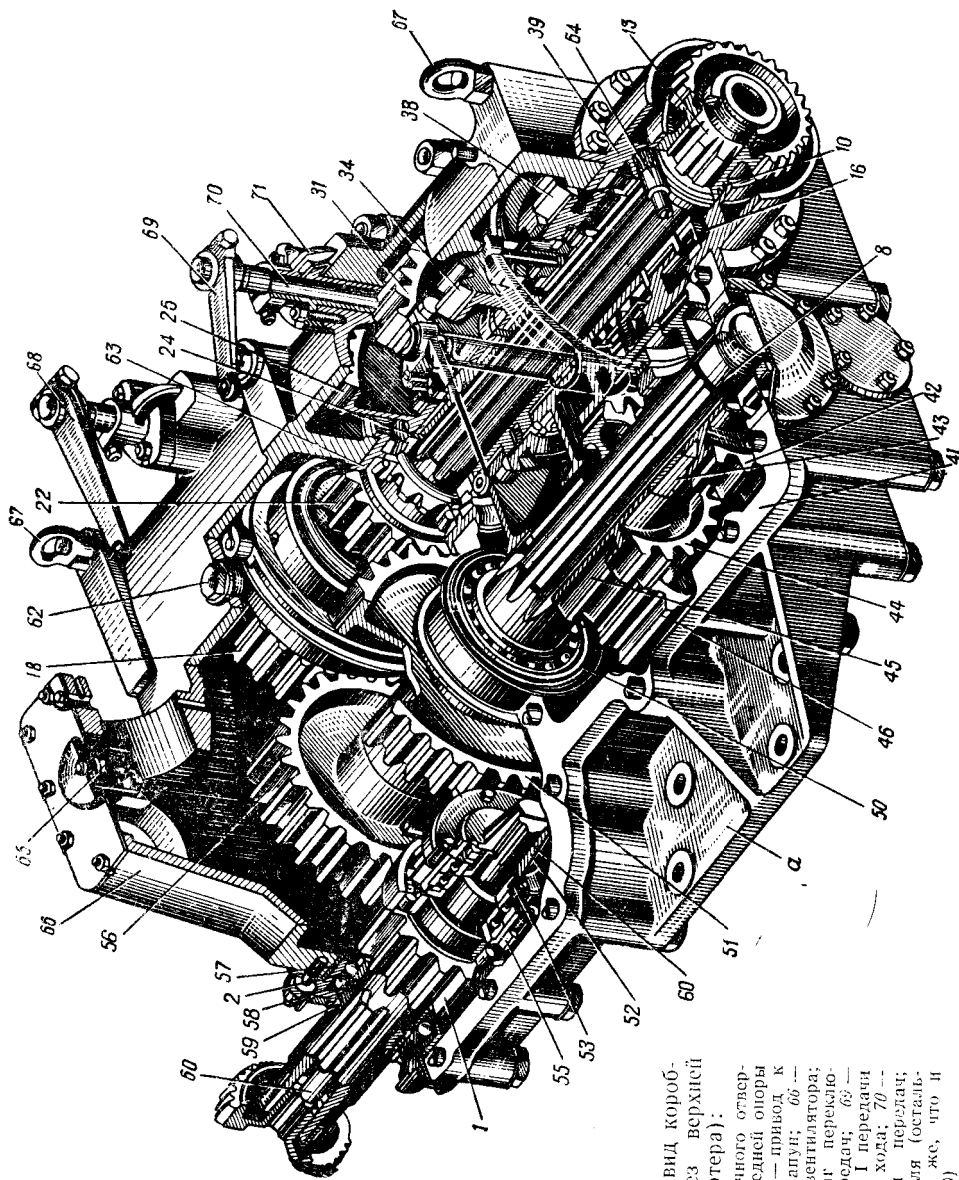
Общий вид коробки передач (без верхней половины картера):
